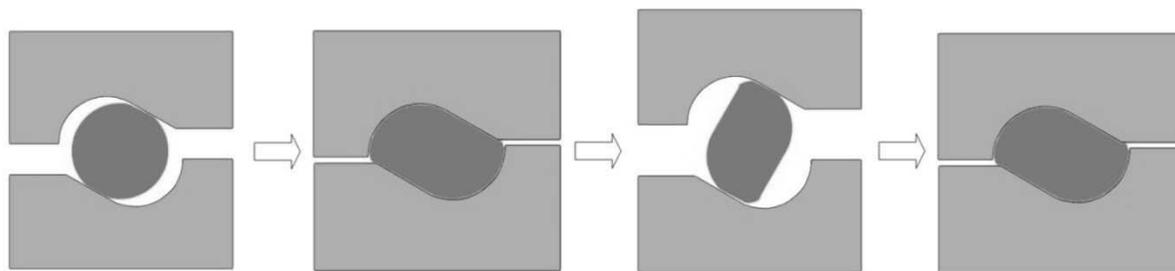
Кузнечный инструмент и схемаковки заготовок в нем
